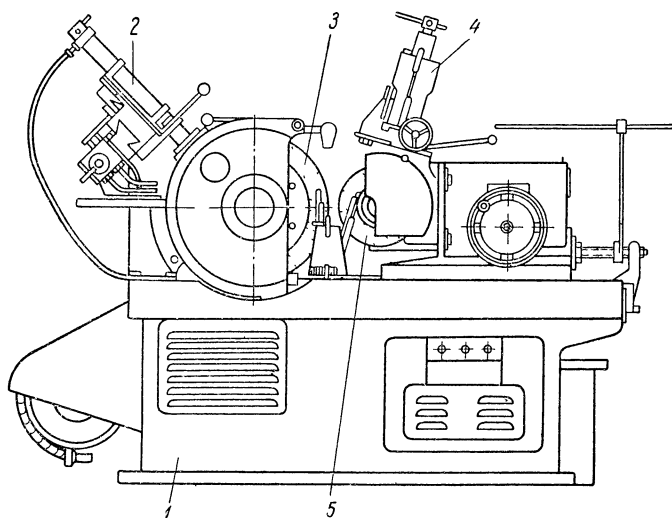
Бесцентровошлифовальный станок модели 3180.
